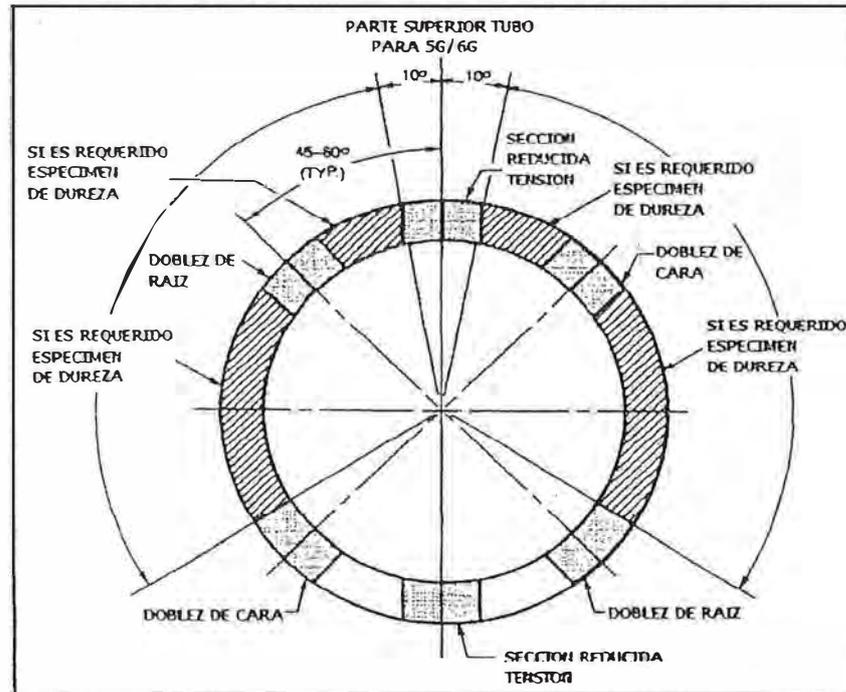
Localización de especímenes de prueba de soldadura en chaflán-tubo
